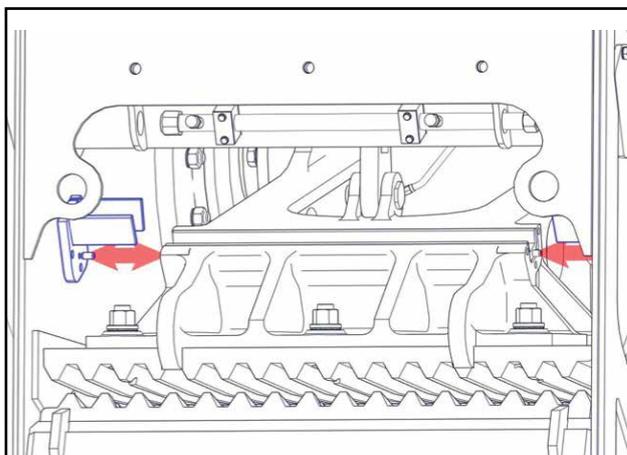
Посадочное место механизма рычажного типа: Демонтаж стопорной пластины
